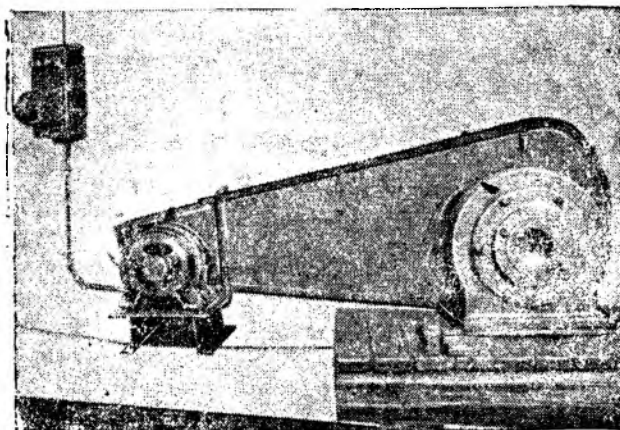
Вальцы для захваток. С правой стороны вальцев укреплено кольцо для проверки толщины захватки
